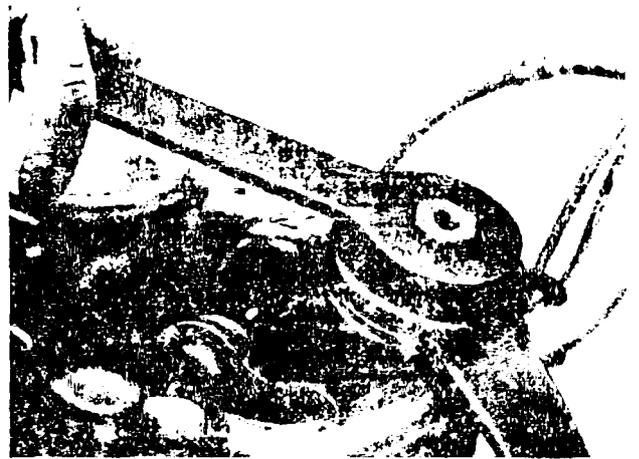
Lösen der kleinen Lenkkopfmutter (26 mm SW) mit Ringschlüssel Nr. 01843
